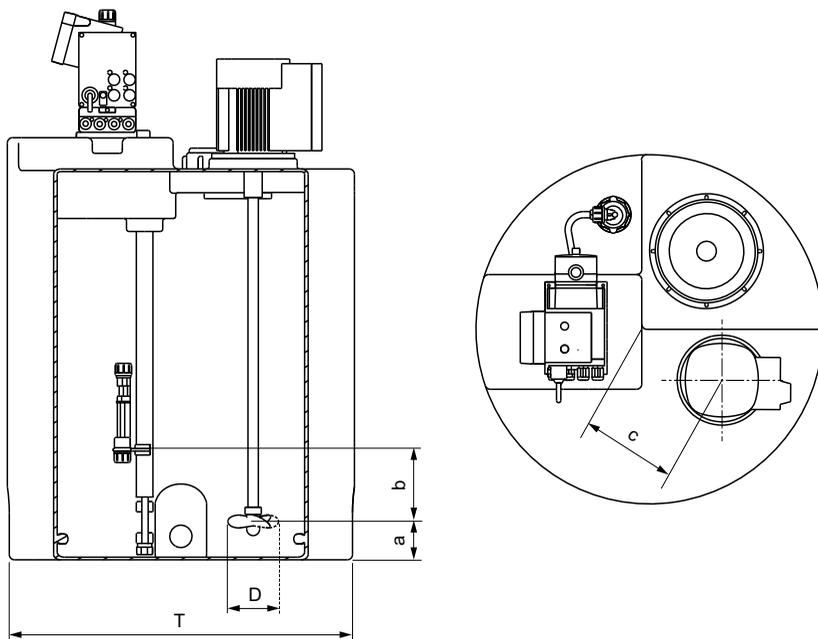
Дозировочный бак в разрезе, продольное сечение и вид сверху
